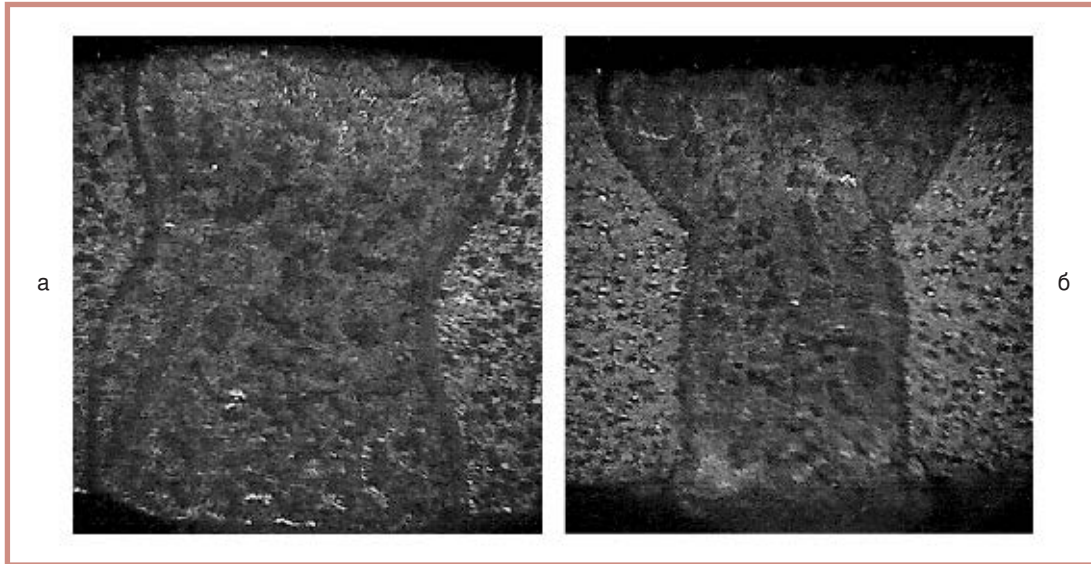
Изменение формы шва при сварке стыковых соединений из стали 10X18H10T ($\delta=1,5$ мм) непрерывным излучением волоконного лазера мощностью 400 Вт: а — защита Ar с расходом 14 л/мин, скорость сварки 30 м/ч, заглупление фокуса 0,3 мм; б — давление $1,5 \cdot 10^{-2}$ торр, скорость сварки 30 м/ч, заглупление фокуса 0,3 мм
